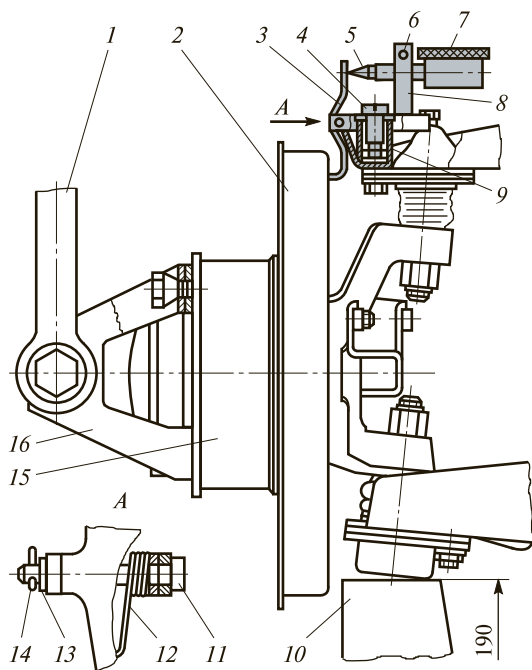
Замер зазора в верхней шаровой опоре с помощью приспособления:
